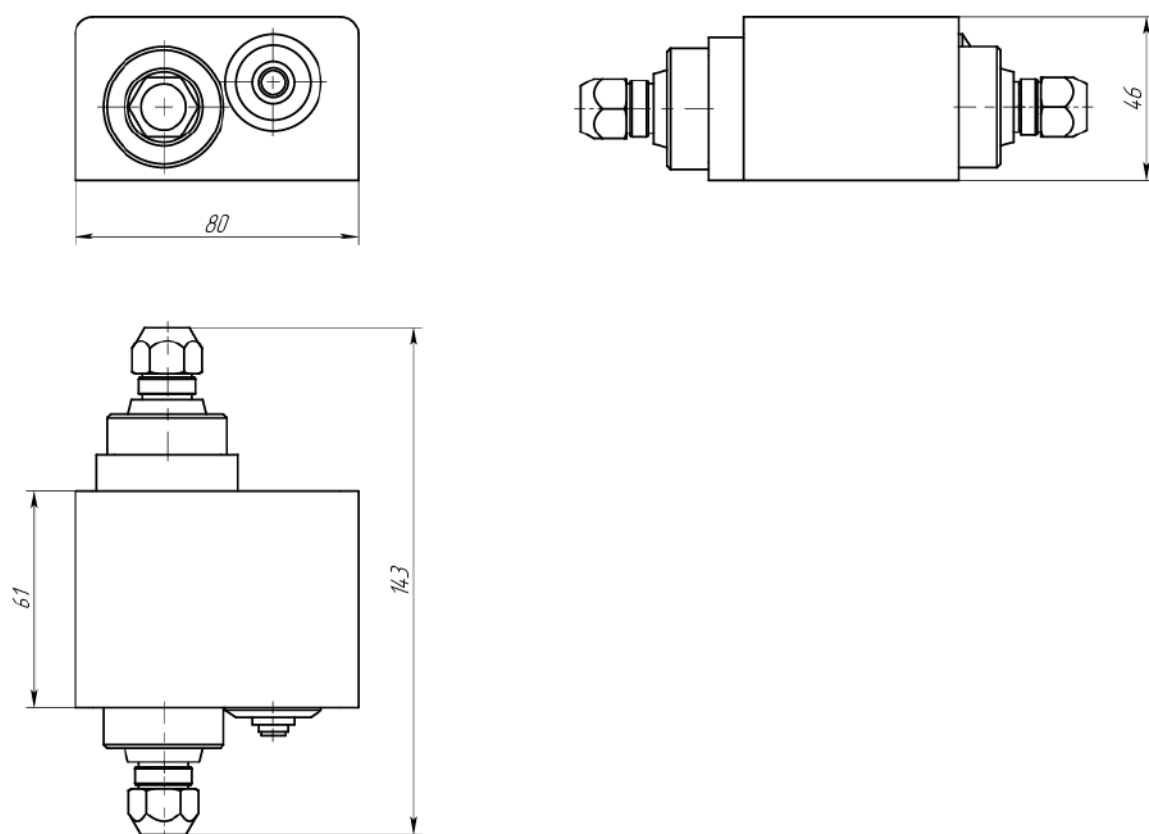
Габаритные и присоединительные размеры реле давления типа РДДф
